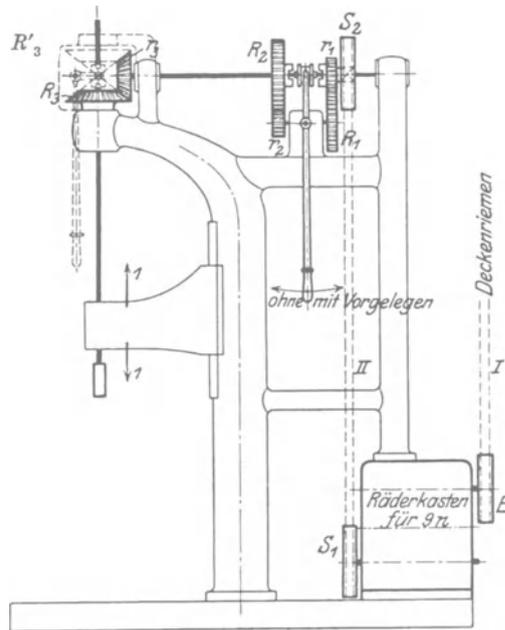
Antrieb der senkrechten Hauptspindel bei einem Säulenständer.
